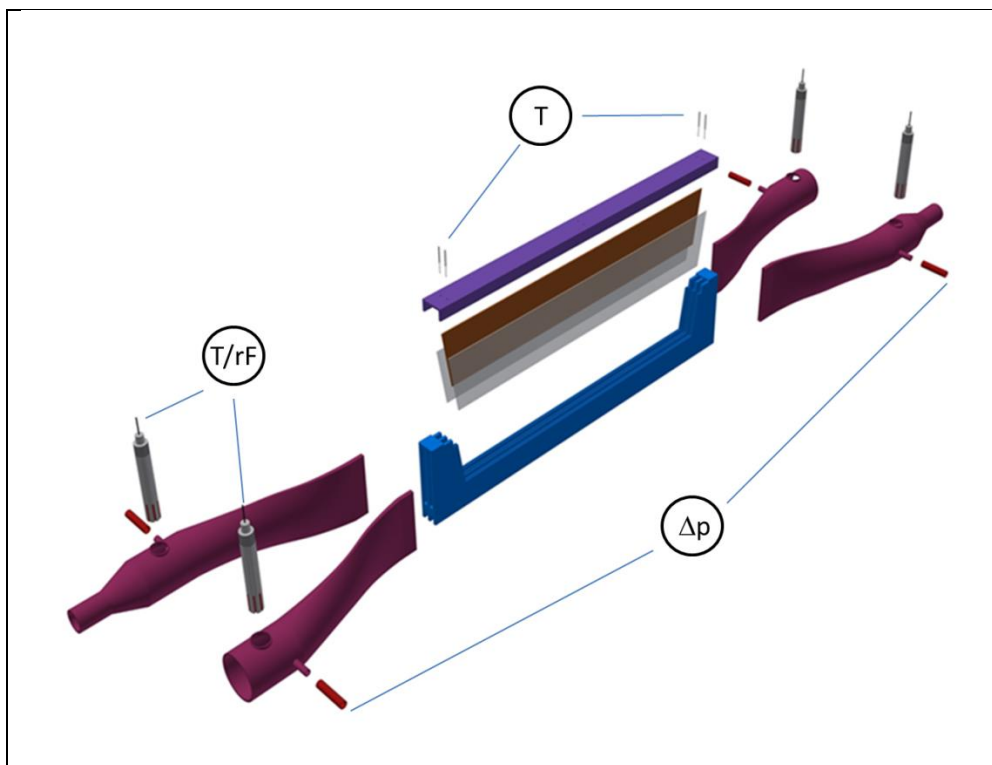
Explosionszeichnung des Testkanals, trapezförmige Mittelwand wechselbar
